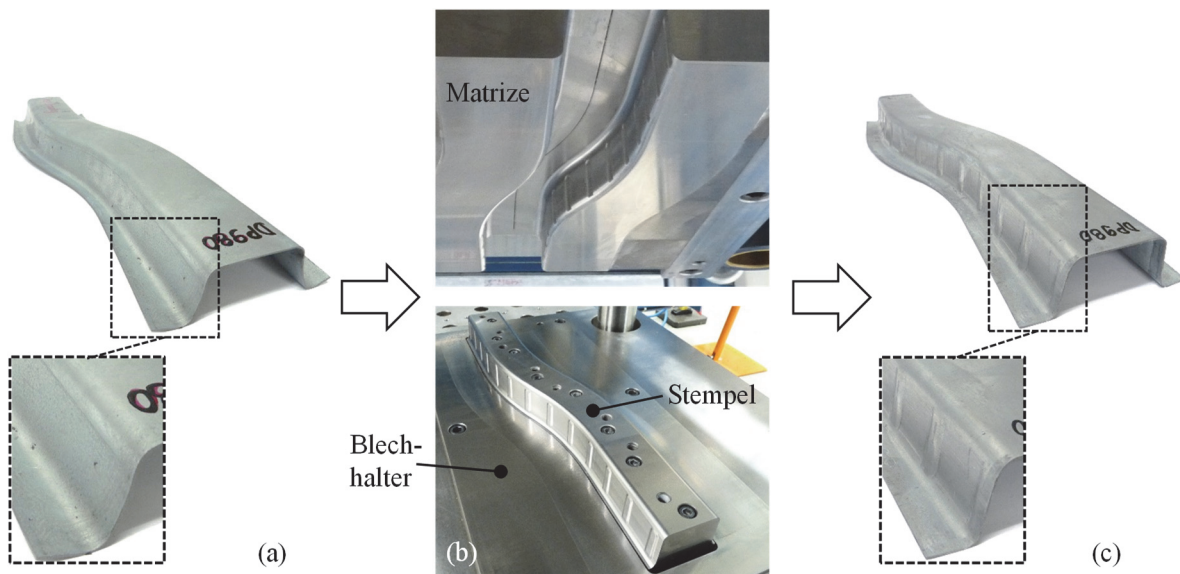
Vorgehensweise für das Nachformen der Bauteilzarge; (a) Bauteil nach dem Tiefziehen, (b) Nachformwerkzeug, (c) Bauteil nach dem Nachformen; Werkstoff DP 980
